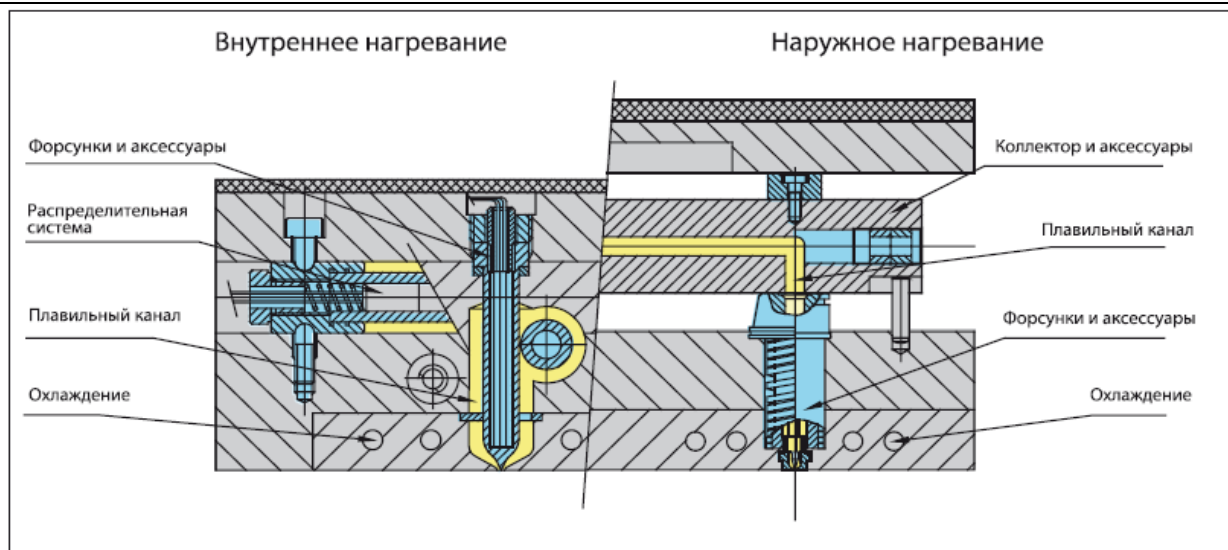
Схематичное изображение конструкций ГКС с внутренним и наружным обогревом.
